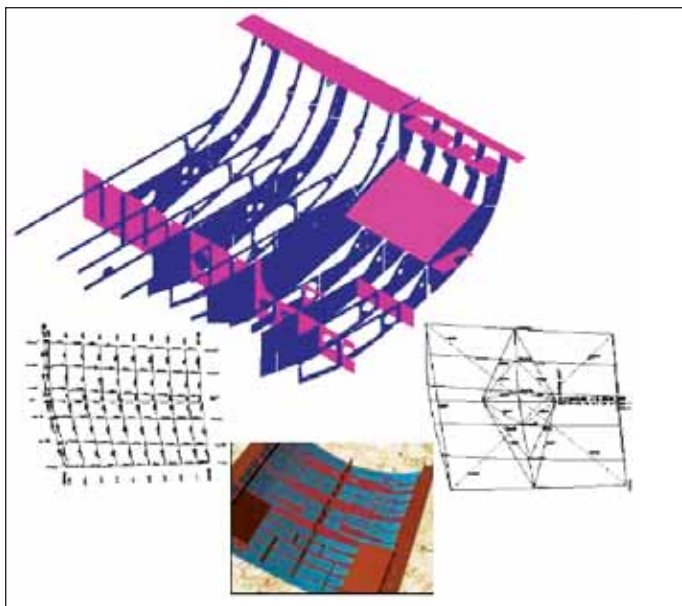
Сборочная оснастка (контуровочный/разметочный эскиз и эскиз для разметки базовых линий)
